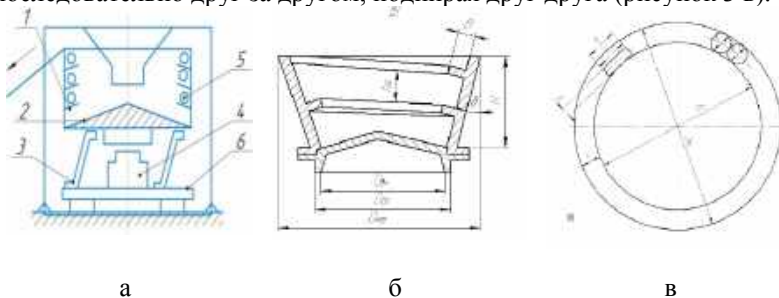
Схема вибробункера и конструкция конического дна: а – схема работы вибробункера; б- главный вид конического дна; в – вид сверху конического дна
